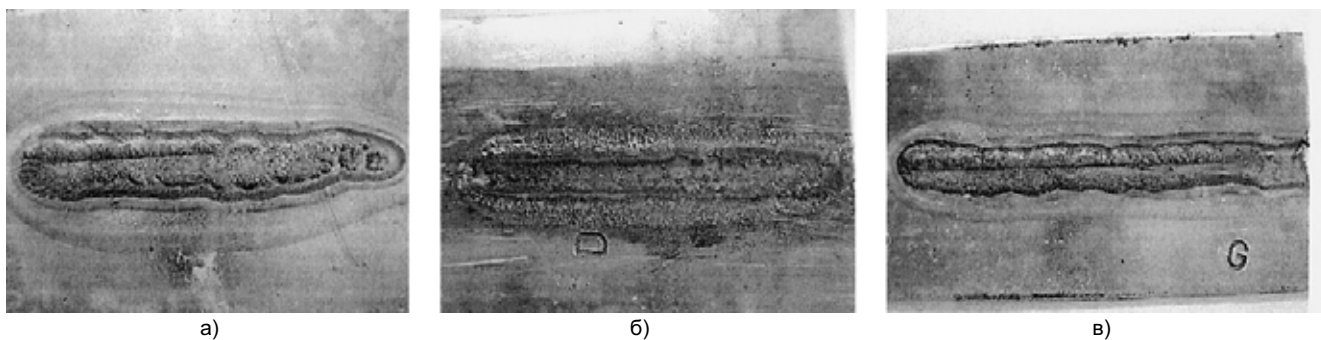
Внешний вид сварного шва при аргонодуговой сварке алюминированной стали: а — без применения флюса; б, в — по слою флюса, содержащего соответственно FeCl_3 и Fe_2O_3
